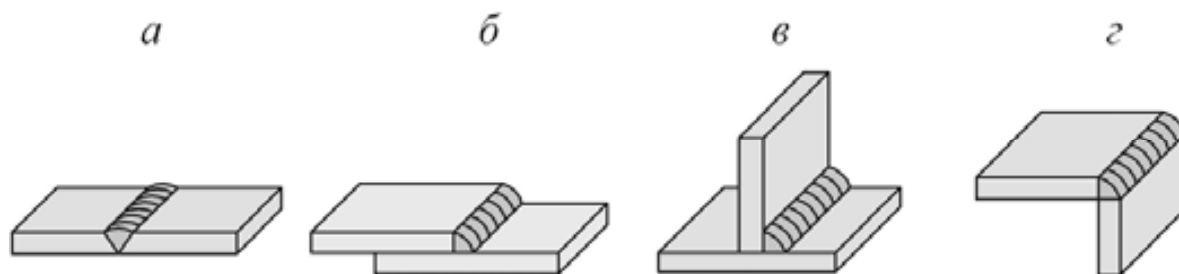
Виды сварных соединений: *а* – стыковое; *б* – нахлесточное; *в* – тавровое; *г* – угловое
